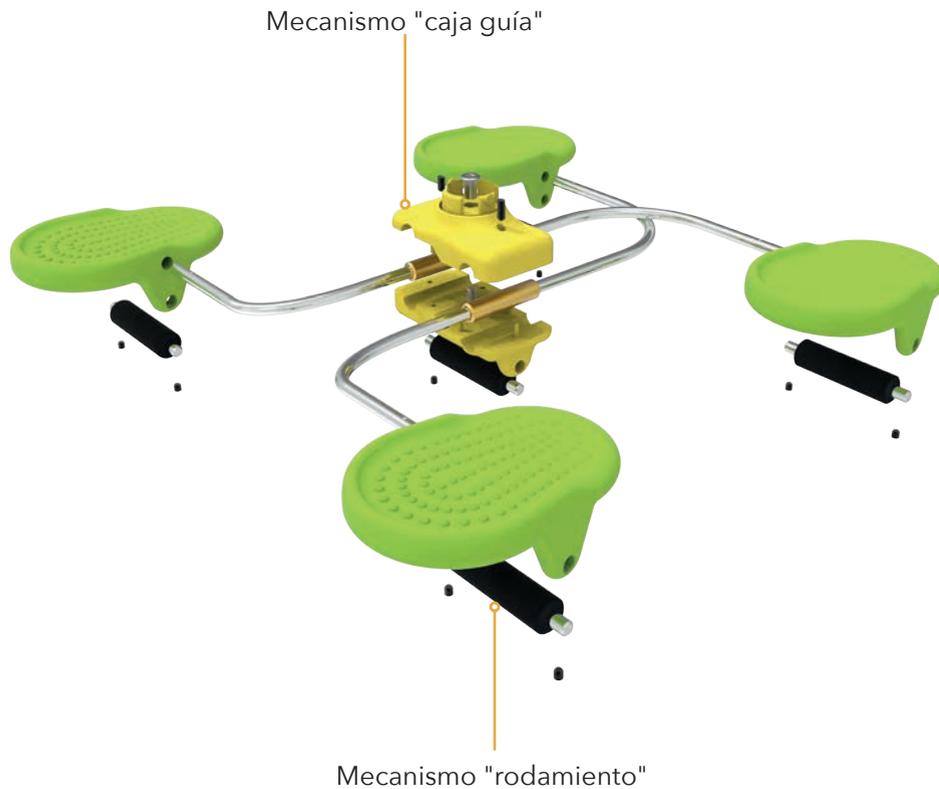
Explosivo del mecanismo de patrón cruzado.
